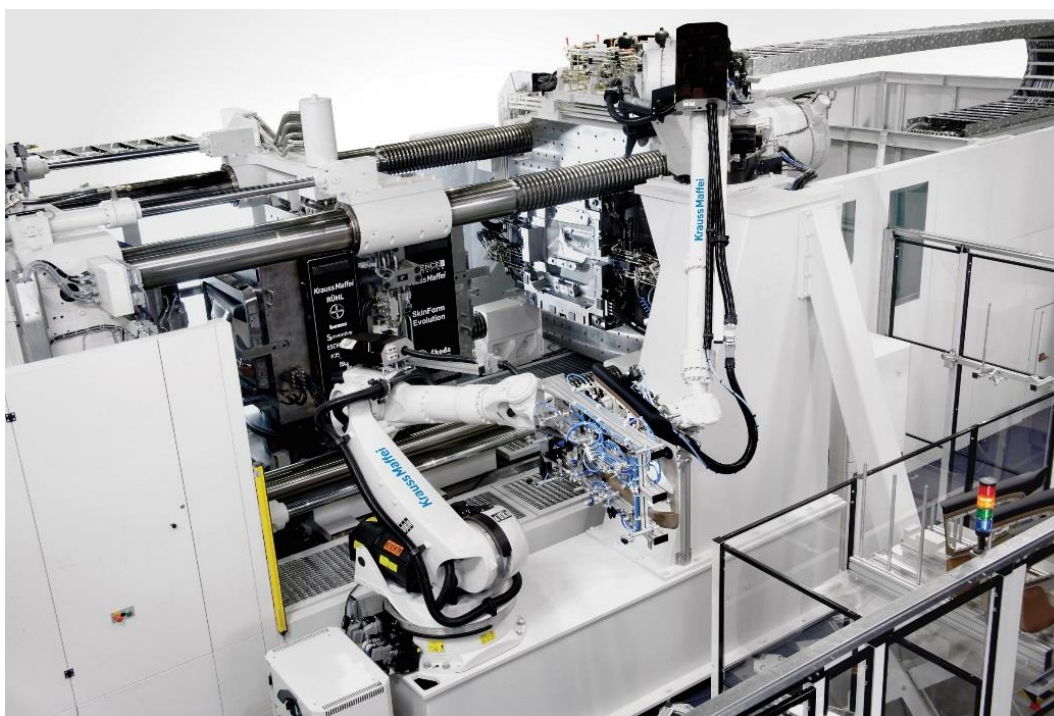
Máquina injetora com robô para extração de componentes [54].
